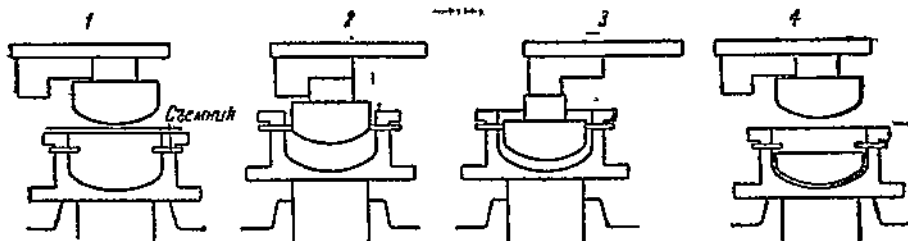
Схема штамповки: 1 — положение пуансона до штамповки, 2 — первая операция, 3 — вторая операция, 4 — положение пуансона после штамповки
